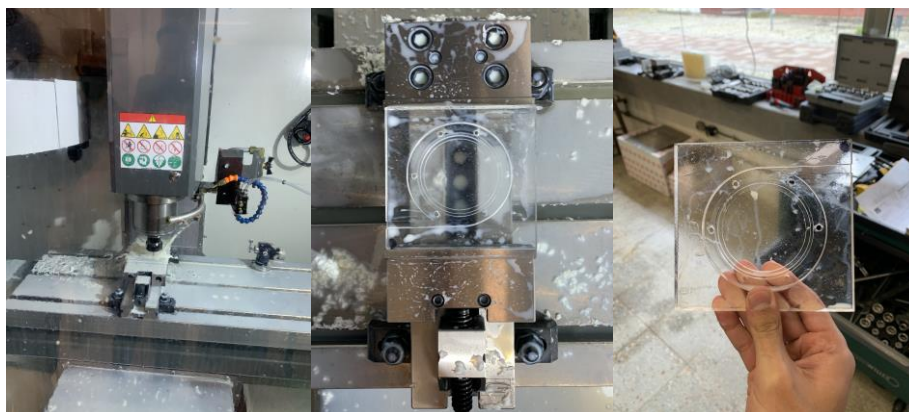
Da esquerda para a direita: maquinação, *setup* visto de cima, bloco maquinado.
